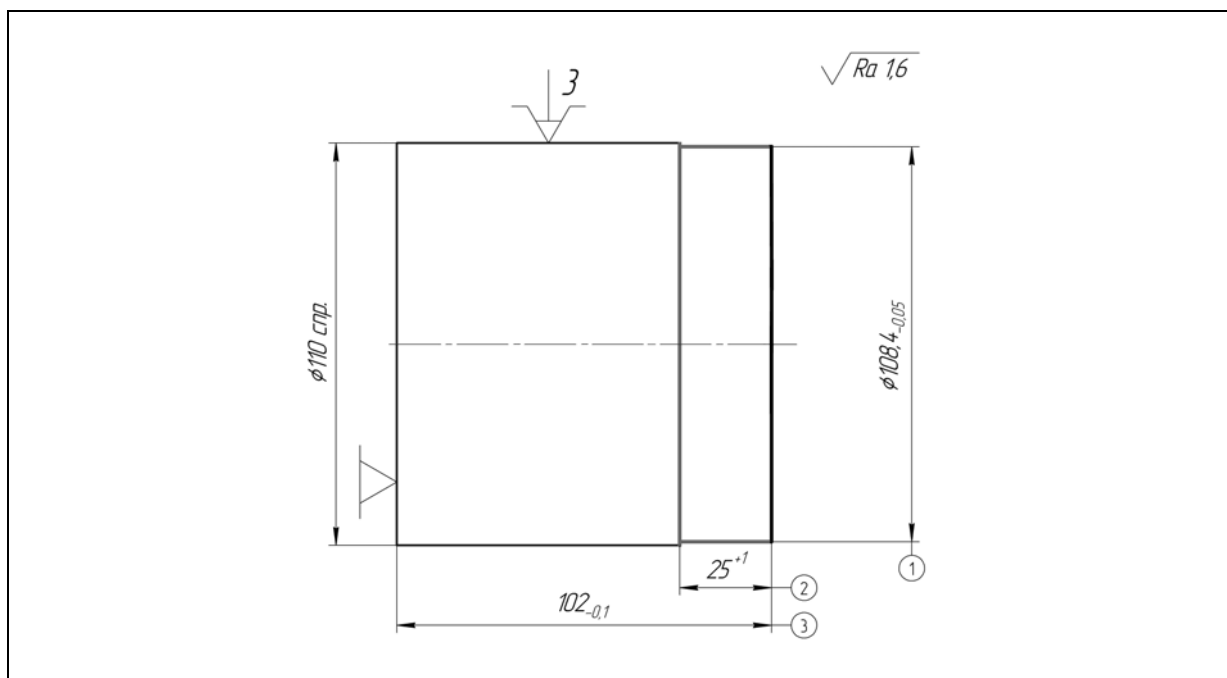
Эскиз обработки детали по предварительной токарной операции
